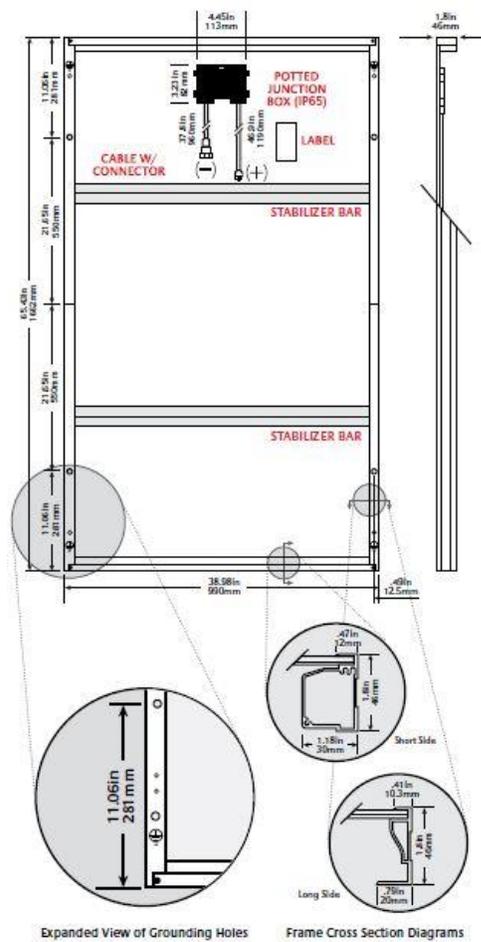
Dimensiones Modulo FV KD250GX-LFB
